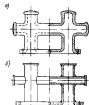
Парные крестовые кнехты: а — литой; б — сварной
